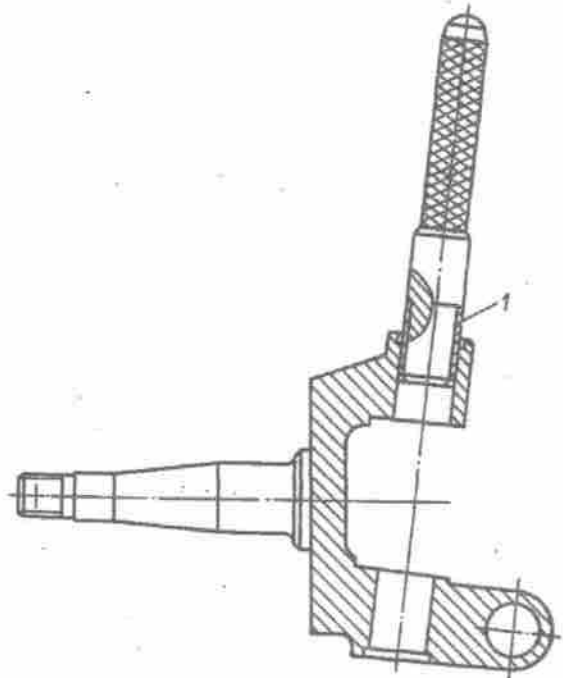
Einpressen der Buchsen des Achsschenkelbolzens:
